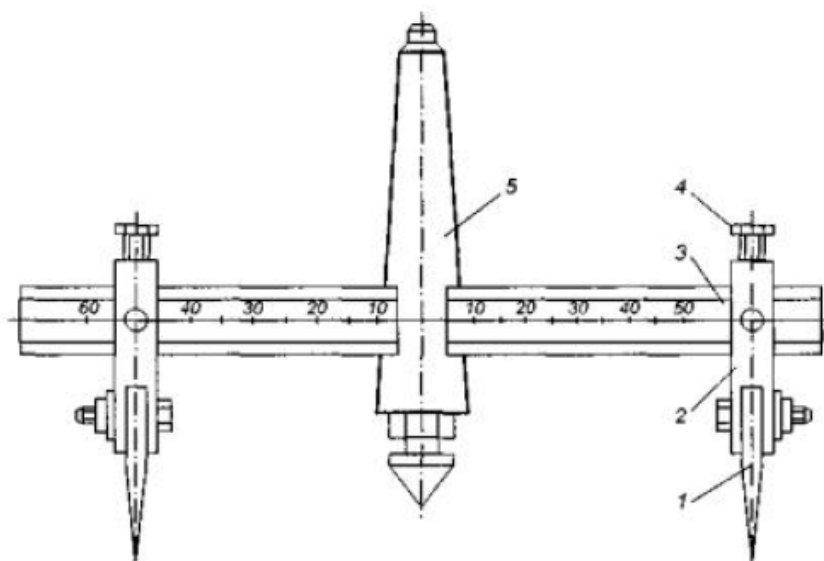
Пристосування для виготовлення прокладок для фланцевих сполук: 1 - ніж; 2 - повзун; 3 - лінійка; 4 - гвинт; 5 - корпус
